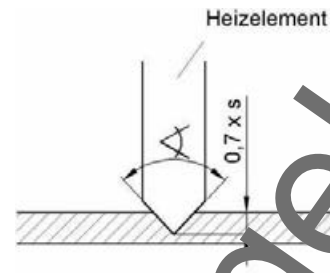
Schwenkbiegeschweißen mit einseitiger Erwärmung (Prinzip).
